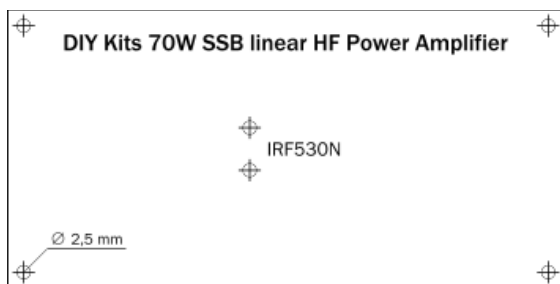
Bohrschablone für den Kühlkörper (nicht Größenrichtig)
